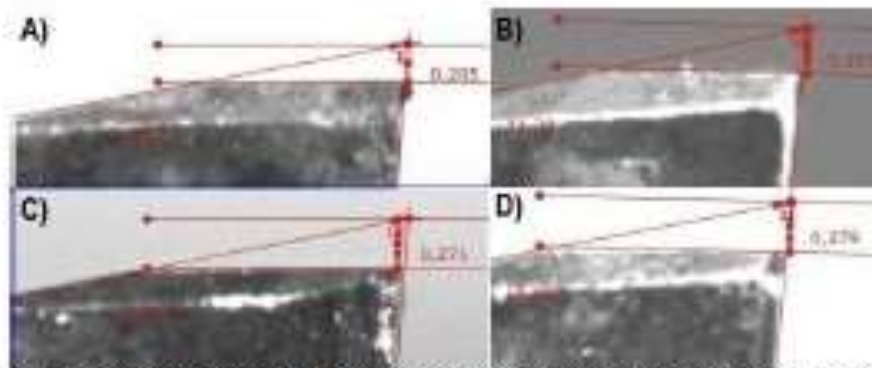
Desgaste del flanco VB de Insertos sin recubrimiento, condiciones de corte: A) 20, B) 30, C) 40 y D) 60m/min
